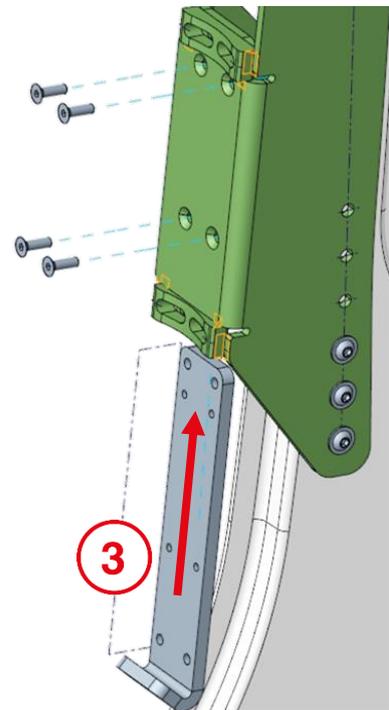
Montage Gewindeplatte; Ansicht Außenseite
